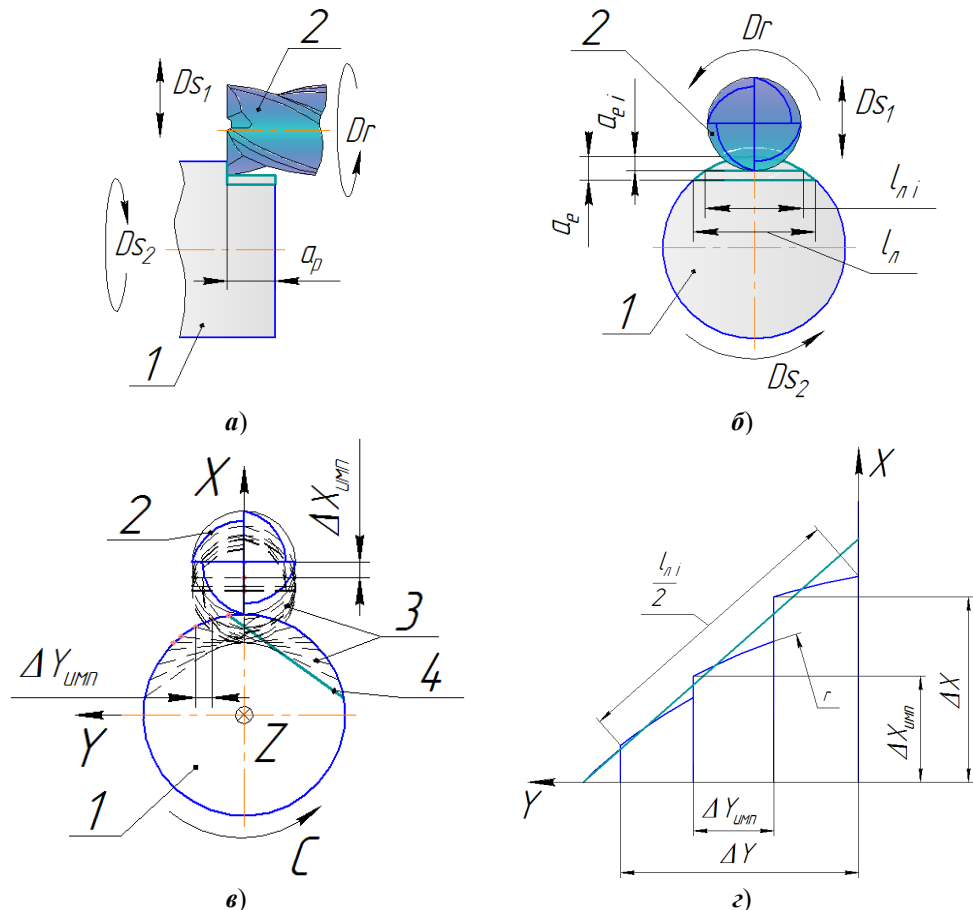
Схемы обработки (а, б) и формирования плоской поверхности (в) с реализацией линейной интерполяции (з) на токарном станке с ЧПУ модели EMCO S45: 1 – деталь; 2 – инструмент; 3 – промежуточные положения детали и инструмента; 4 – номинальная плоская поверхность
